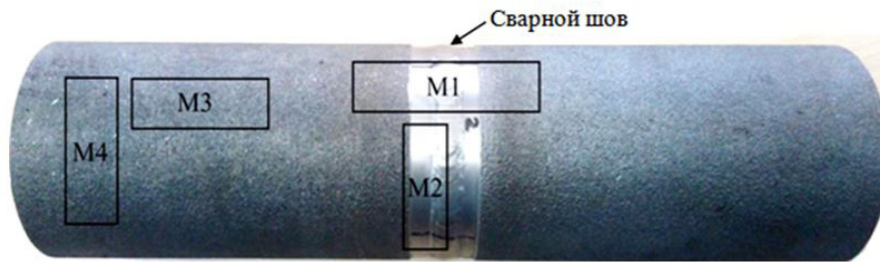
Участки вырезки образцов из трубного сварного соединения для металлографического анализа и измерения микротвердости сплава
